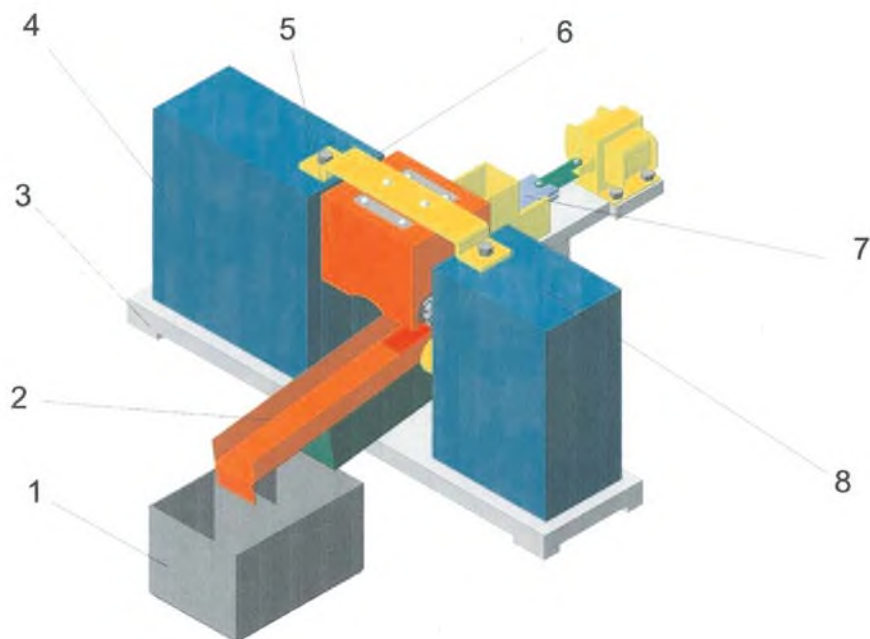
Общий вид автомата: 1 – бункер; 2 – механизм разброски; 3 – станина; 4 – блок левый; 5 – узел оптического контроля; 6 – планка; 7 – механизм поштучной выдачи; 8 – блок правый
